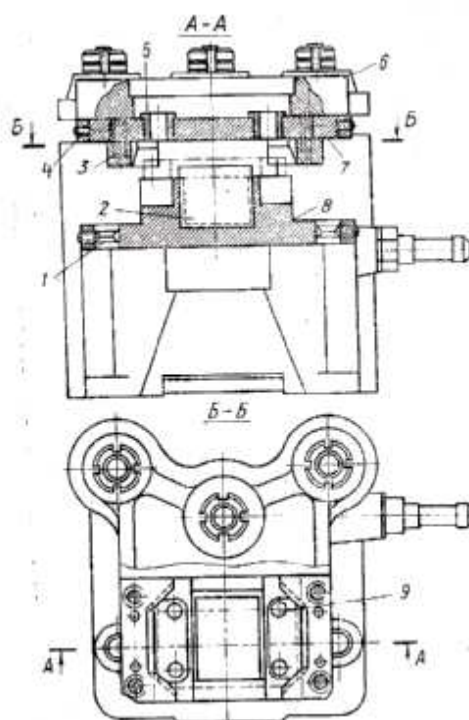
Схема установки і закріплення змінної наладки в скалковому кондукторі консольного типу з пневматичним приводом
